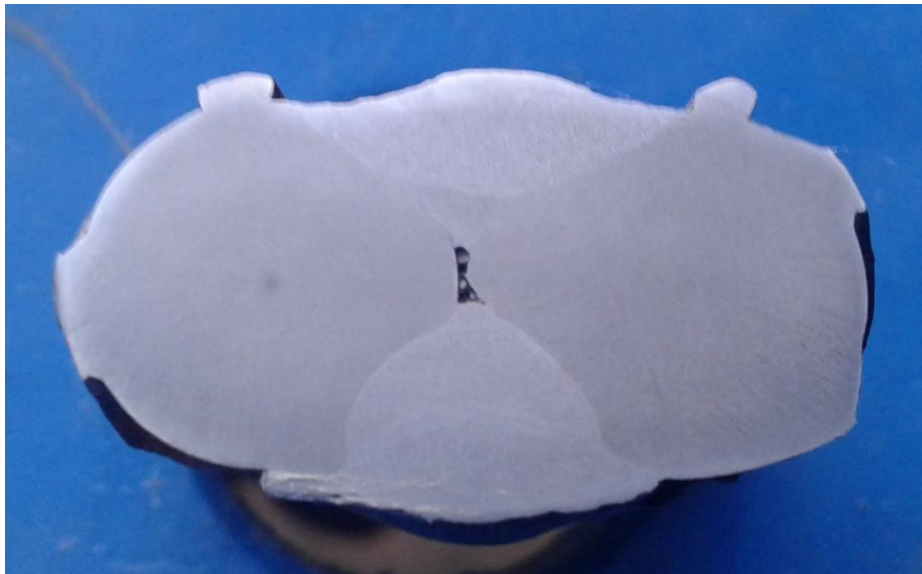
Soldado a solape, vemos la penetración de la soldadura
